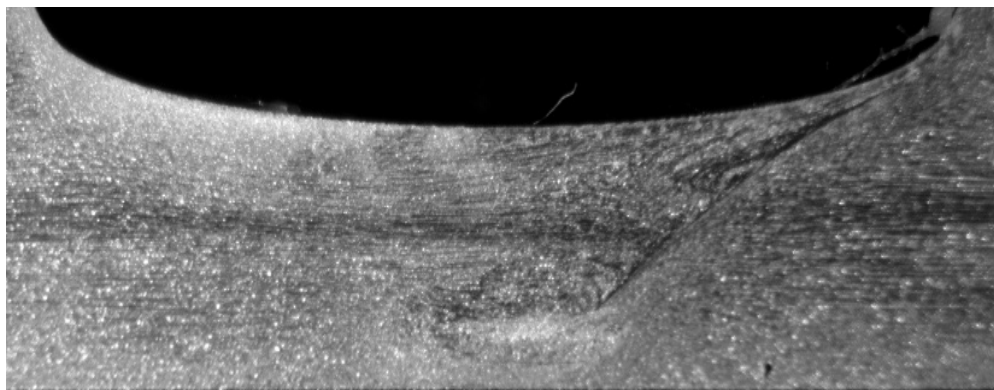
Макрошлиф сварного соединения при угле наклона инструмента к вертикали 10°
